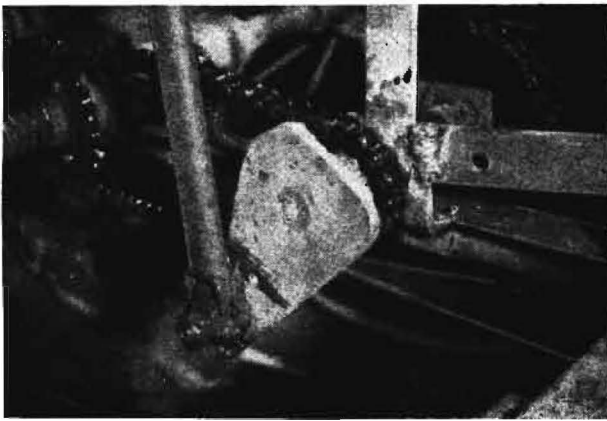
Exzenter ist stirnseitig auf die Achse des inneren Zahnrades der Auslösevorrichtung aufgeschweißt. Am Exzenter ist das Pleuel der CL verstellbar angeschraubt
